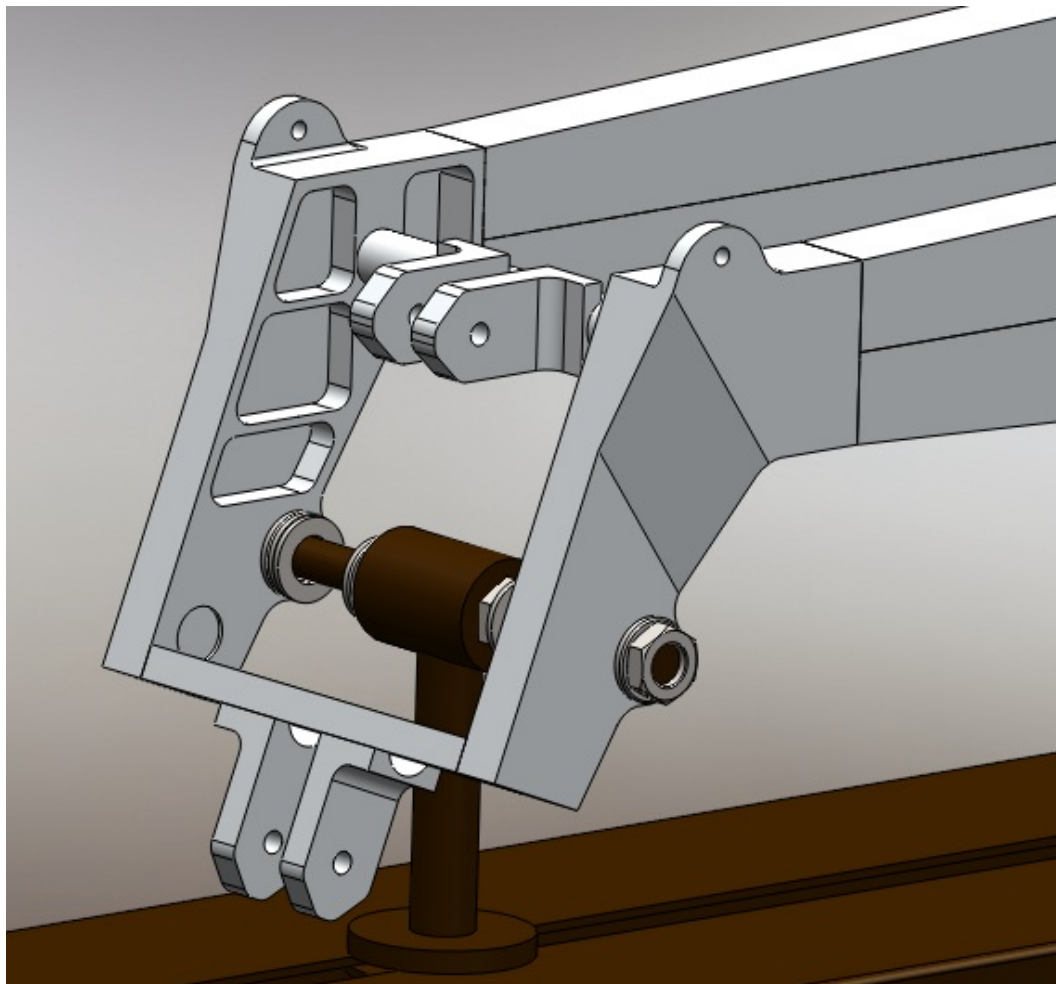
Soldadura del perfil y las pletinas
